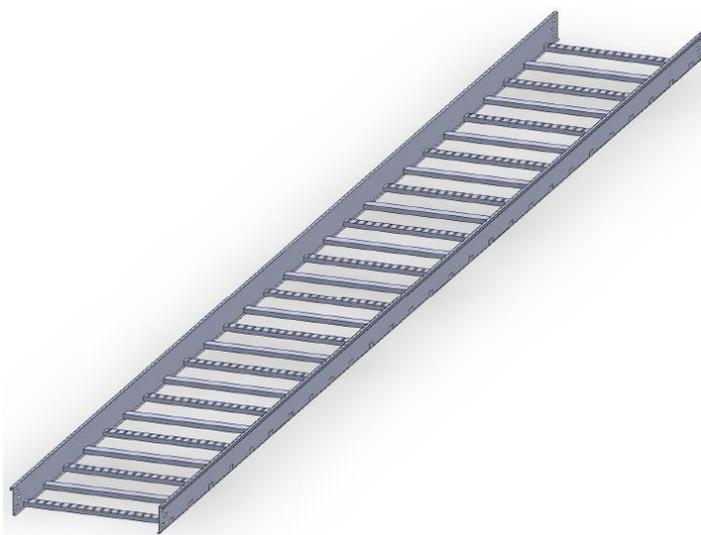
Bandeja Porta cables Tipo Escalerilla en Aluminio longitud 6m, altura 6" y ancho 24".
